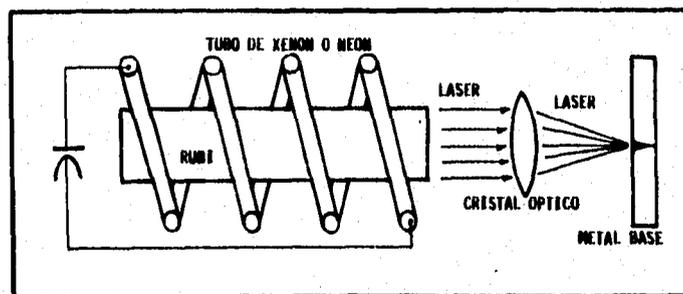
DETALLE DEL PROCESO DE SOLDADURA LBW.
